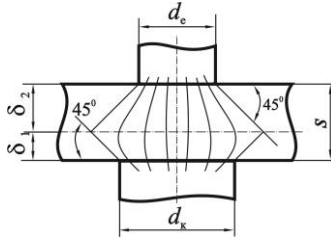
Схема поля струму для розрахунку опору деталі з неоднаковими розмірами контактів
